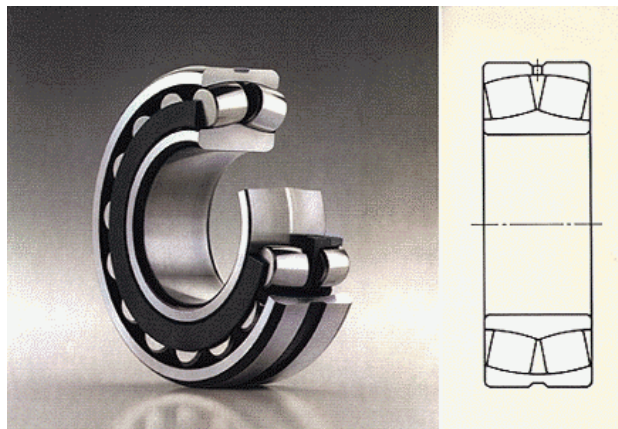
Rodamiento oscilante de rodillos (o de rodillos esféricos) de doble hilera
